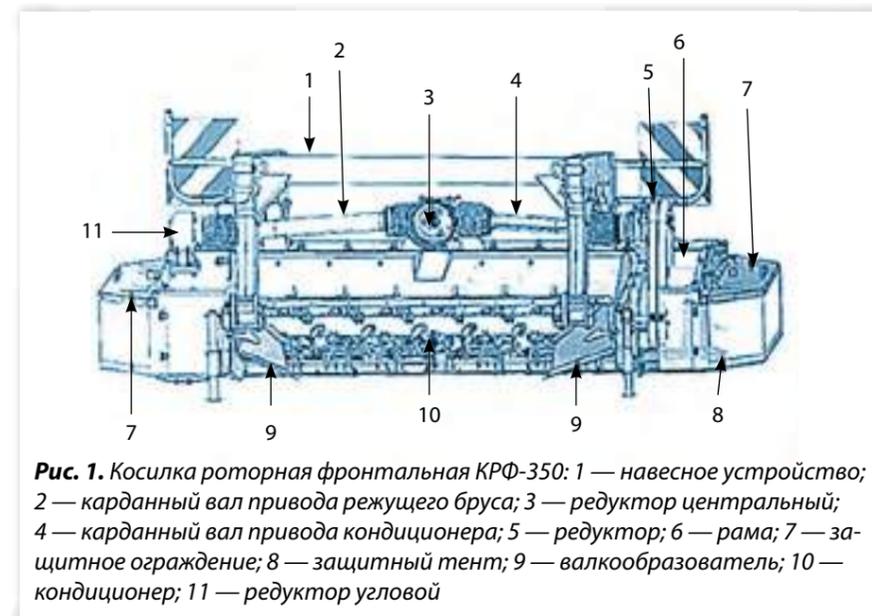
Косилка роторная фронтальная КРФ-350: 1 — навесное устройство; 2 — карданный вал привода режущего бруса; 3 — редуктор центральный; 4 — карданный вал привода кондиционера; 5 — редуктор; 6 — рама; 7 — защитное ограждение; 8 — защитный тент; 9 — валкообразователь; 10 — кондиционер; 11 — редуктор угловой
